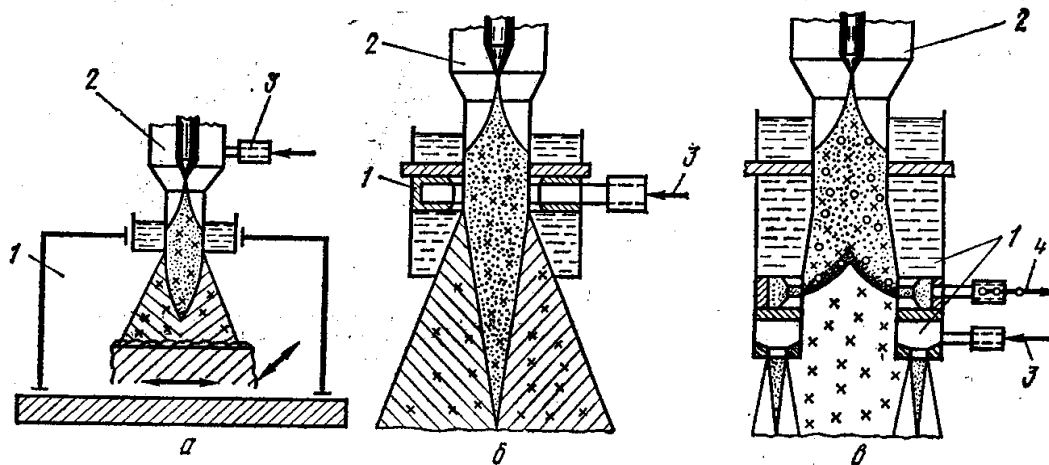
Схеми плазмового напилення з місцевим захистом: а - місцева камера, б - струменевий захист з сопла, в - струменевий кільцевий захист з насадки; 1- місцева камера, сопло, насадка; 2- плазмовий розпилювач; 3 - подача захисного газу; 4 - відсмоктування ПС
